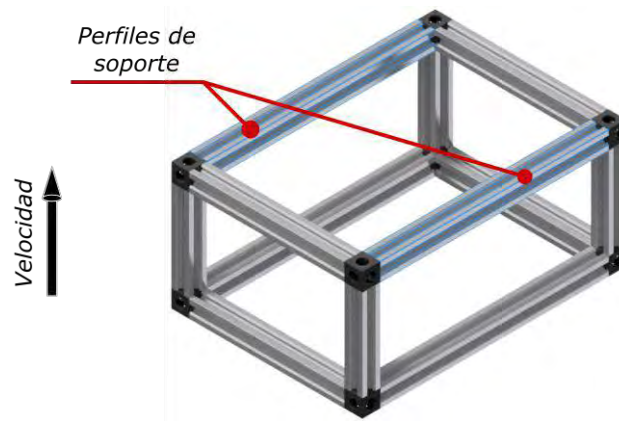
Ubicación de los perfiles de soporte de cargas (Fuente: Elaboración propia).
